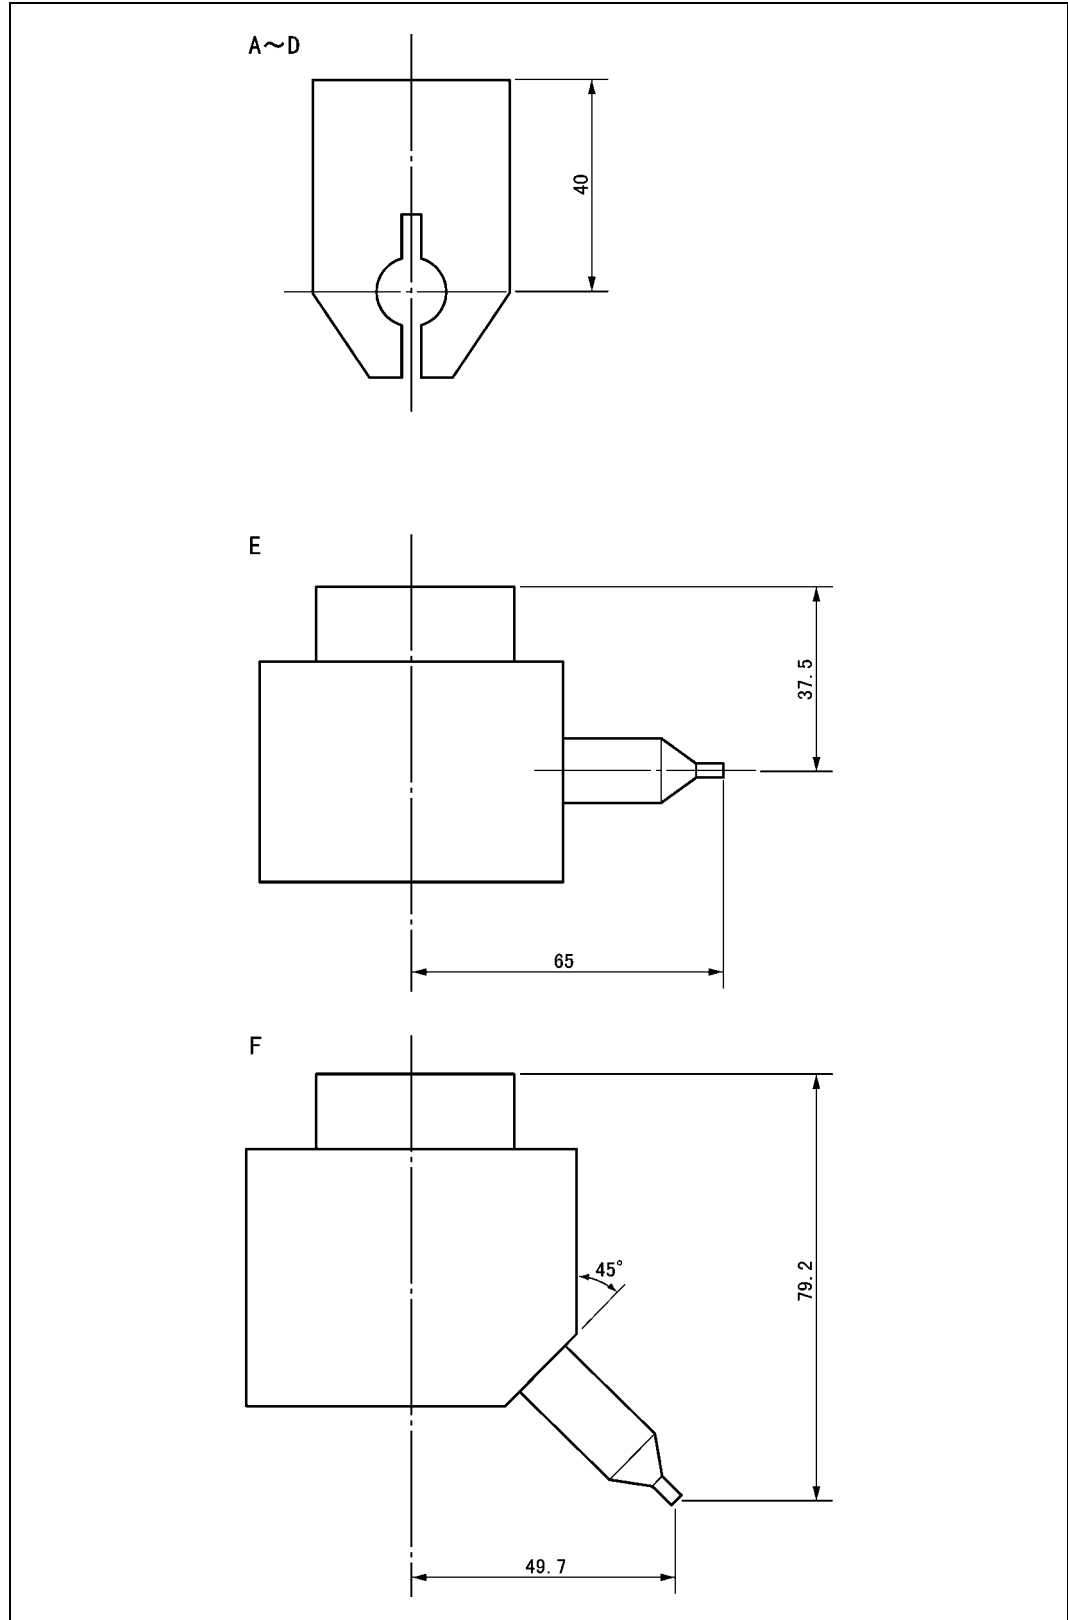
Endwerkzeugtypen mit dem jeweiligen Koordinatenursprung
